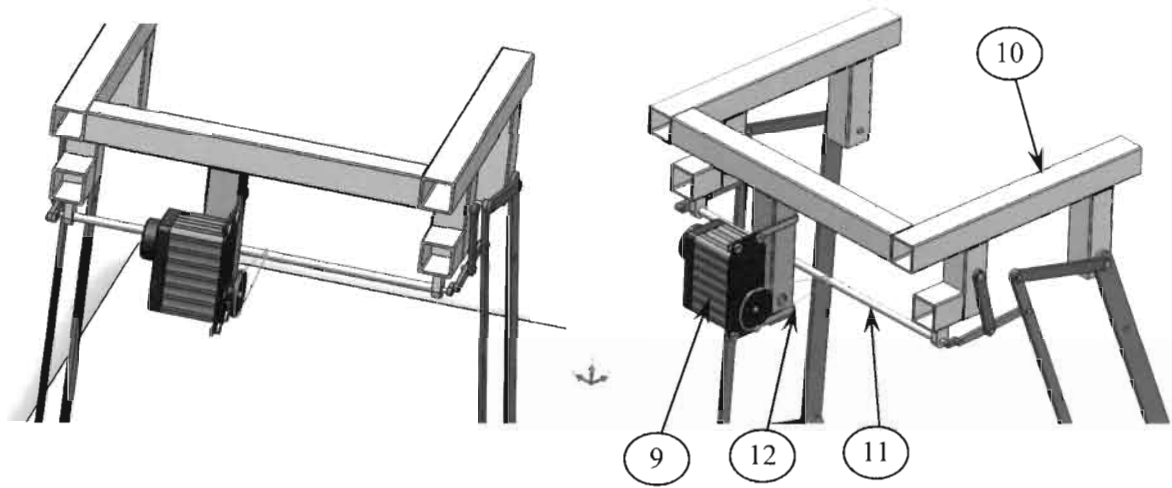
Vedere de detaliu a cadrului superior, cu motorul de acționare.
